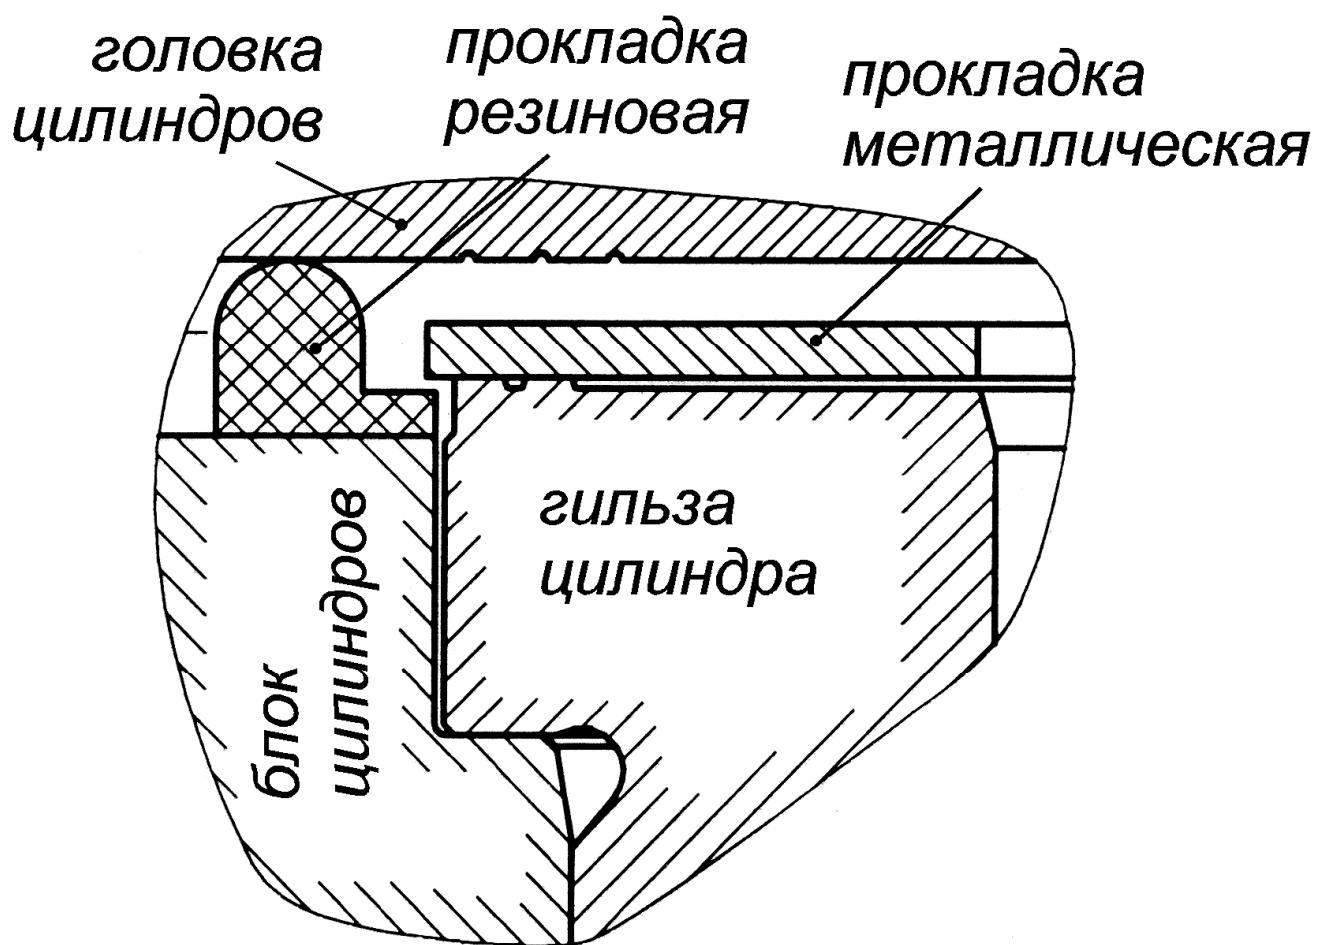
Схема расположения деталей в месте уплотнения газового стыка
